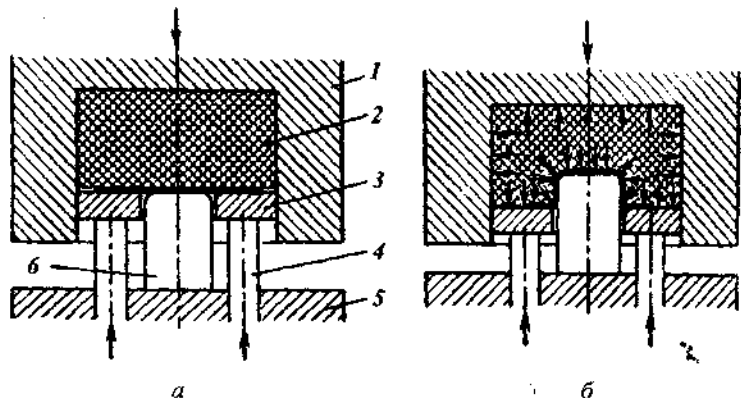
Схема вытяжки эластичной матрицей: а - начальный момент; б - завершение (/ - контейнер, 2 - резина, 3 - прижимное кольцо, 4 - толкатель, 5 - подштамповочная плита, 6 - пуансон)
